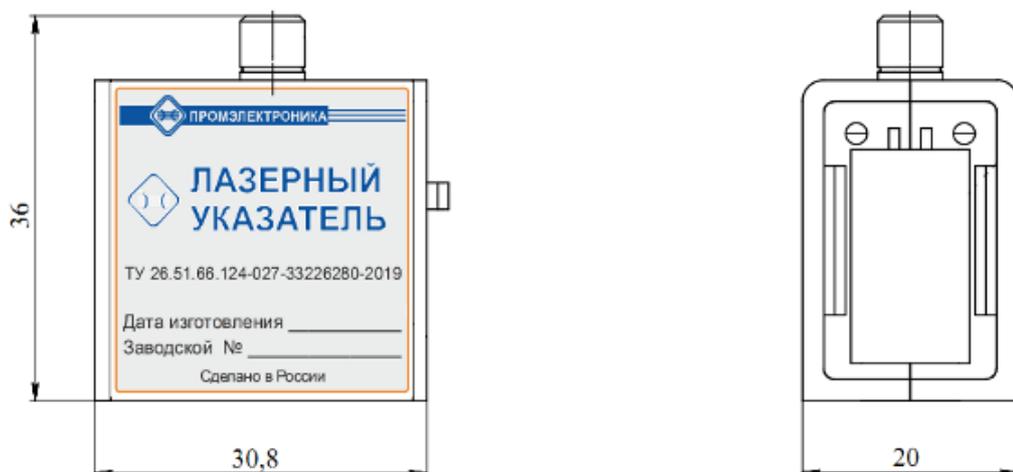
Габаритные размеры лазерного указателя ЛУ-01
